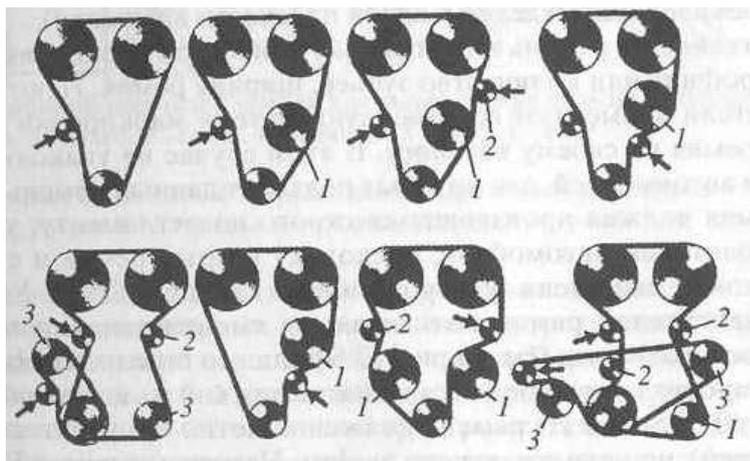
Основные схемы ременного привода распределительного механизма с двумя верхними валами.
